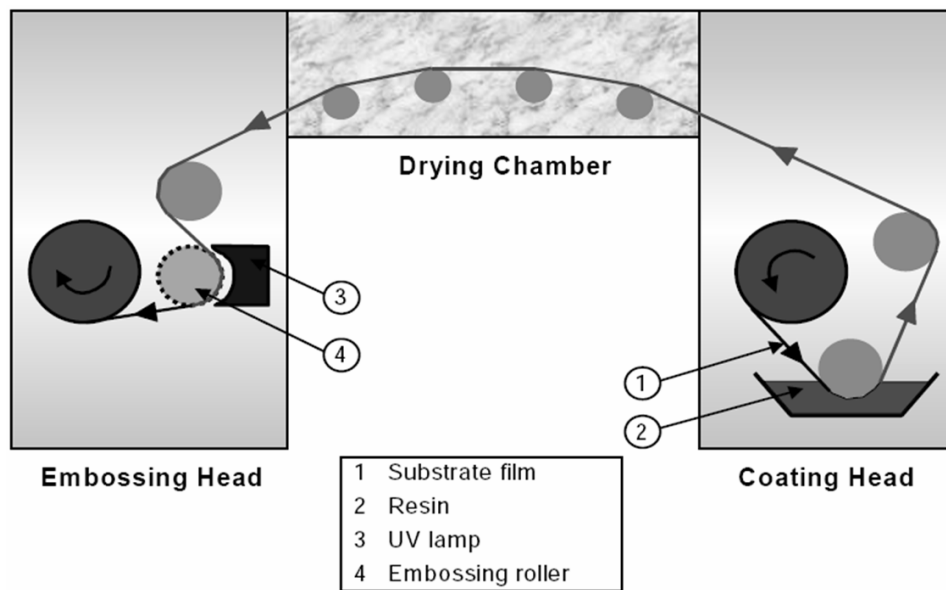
Konzept des Reel-to-Reel Embossing [101]
